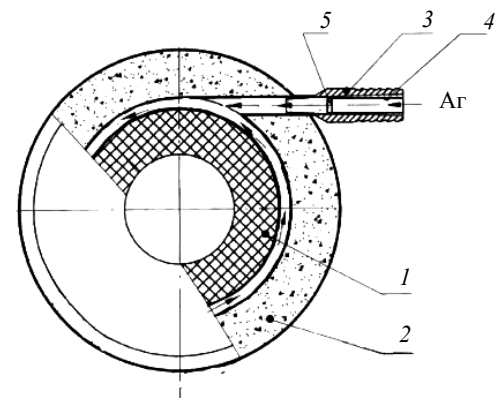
Схема устройства для защиты струи металла при непрерывной разливке:
